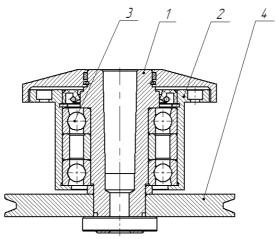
Нижний центр: 1 — шпиндель; 2 — корпус; 3 — подшипники; 4 — шкиф
